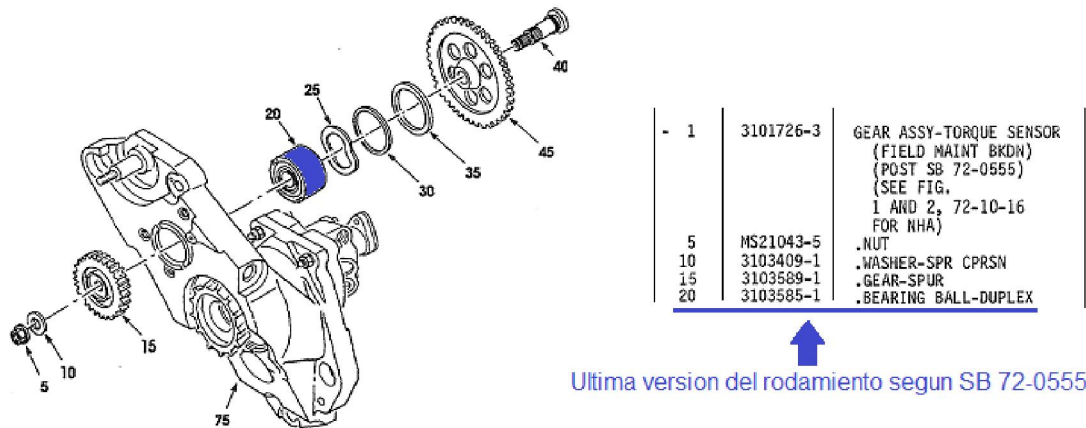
Ensamblaje de Generador de taquímetro y sensor de torque posterior a la aplicación del SB 72-0555 (resaltado en azul sobre el dibujo la última versión del rodamiento en cuestión).
